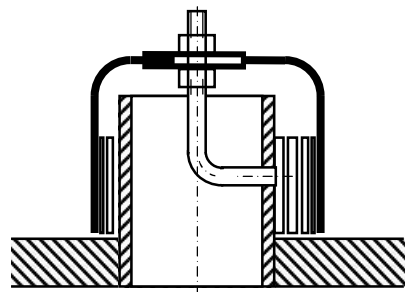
Конструкція ковпачка згідно з пат. № UA150572U
